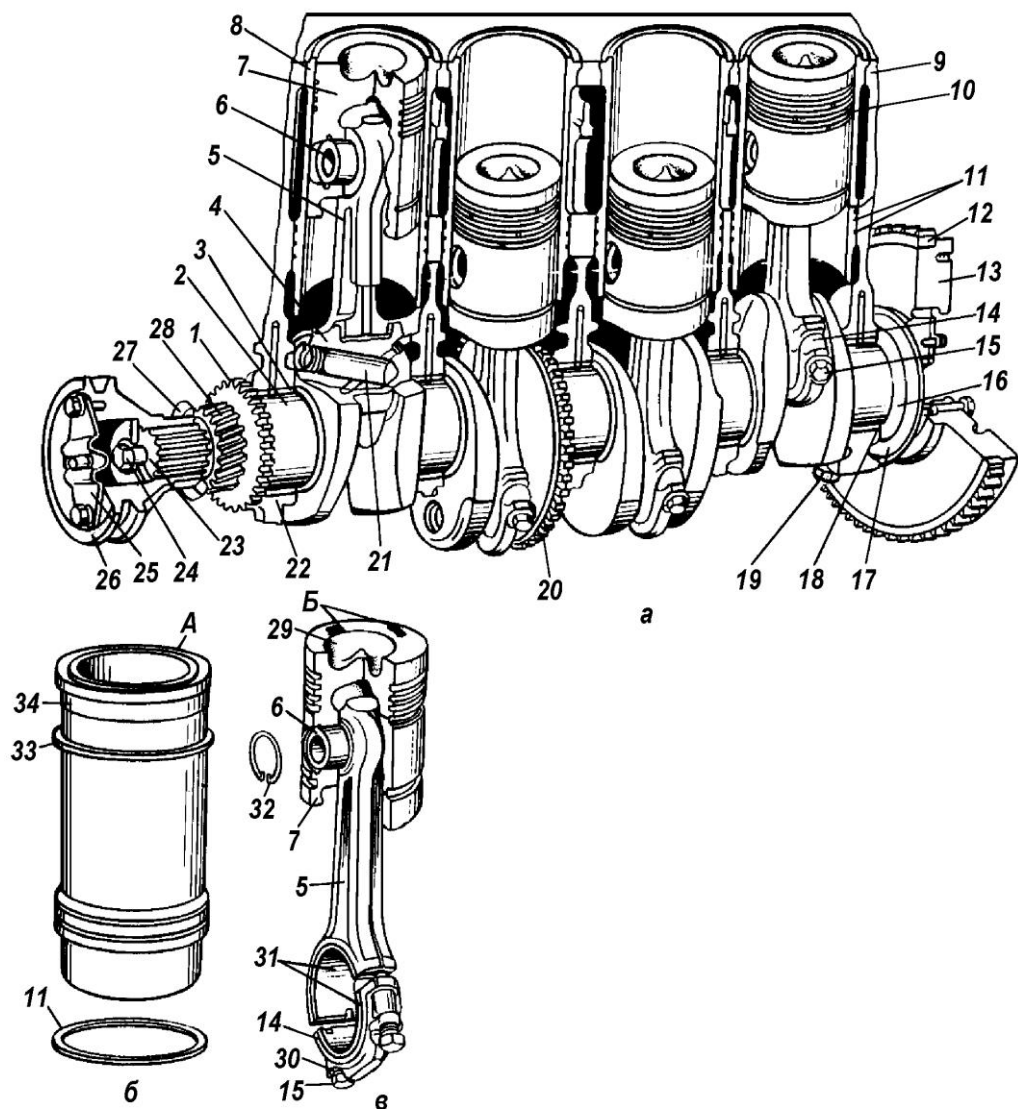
Кривошипно-шатунный механизм в сборе:
